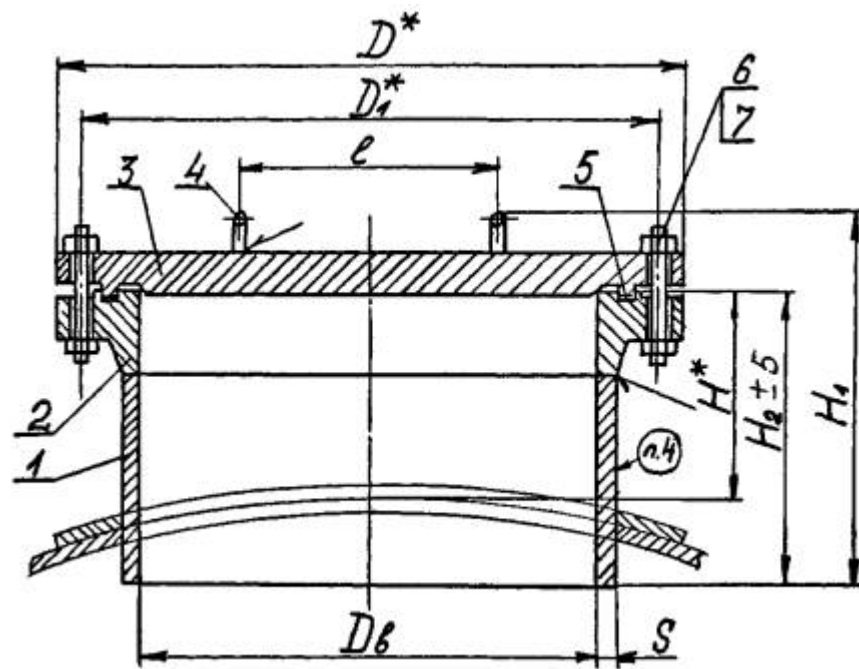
Рисунок люк-лак с уплотнительной поверхностью шип-паз с конструктивными размерами
